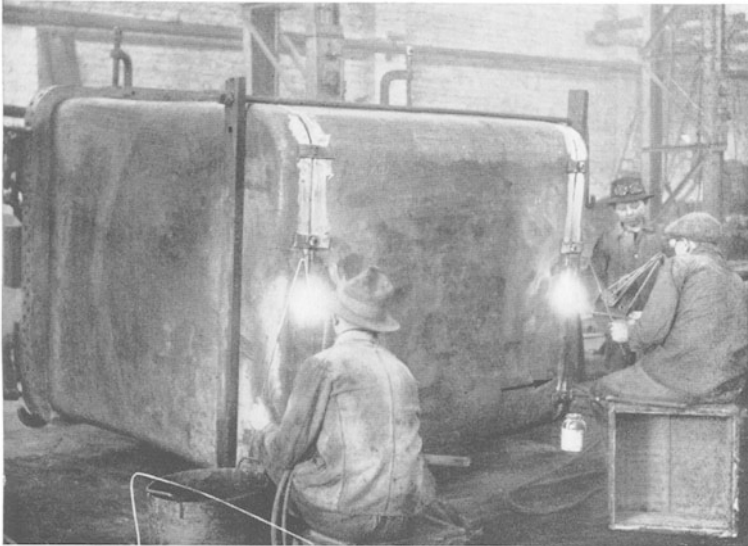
Schweißung einer kupfernen Lokomotivfeuerbuchse.
